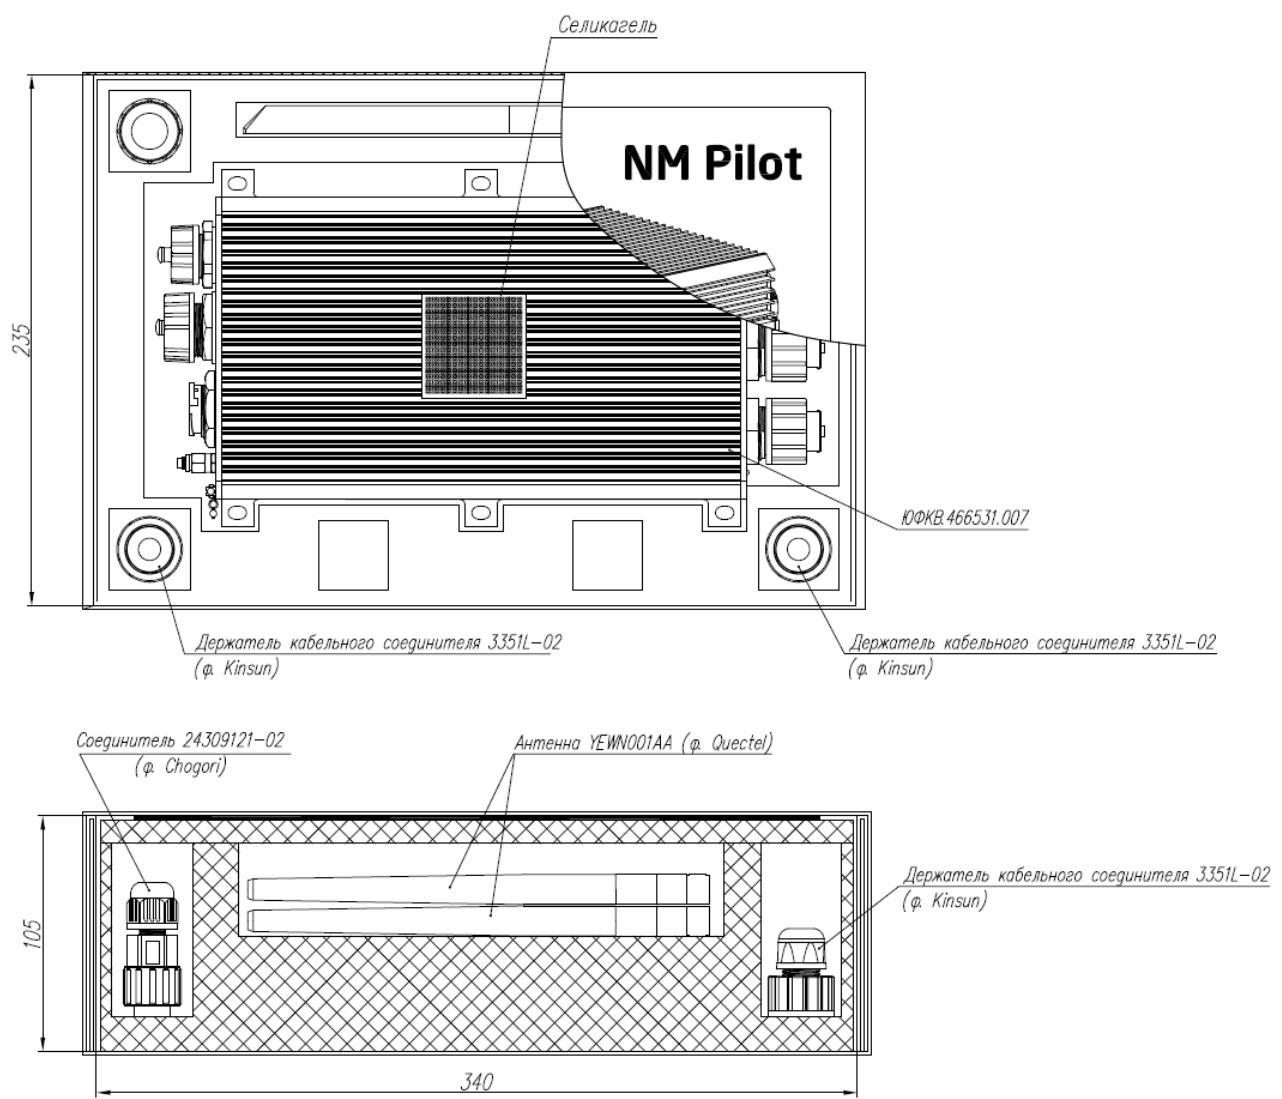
Габаритные размеры упаковки Изделия
